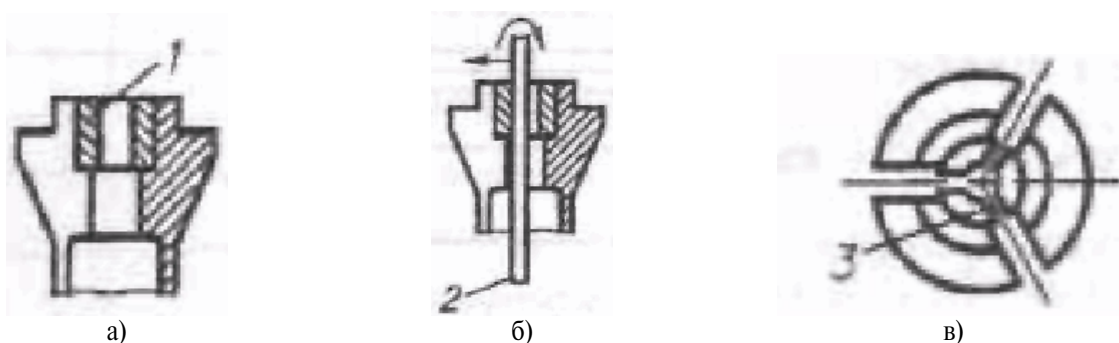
Основные стадии изготовления цанг с диаметром рабочего отверстия более 1 мм:
